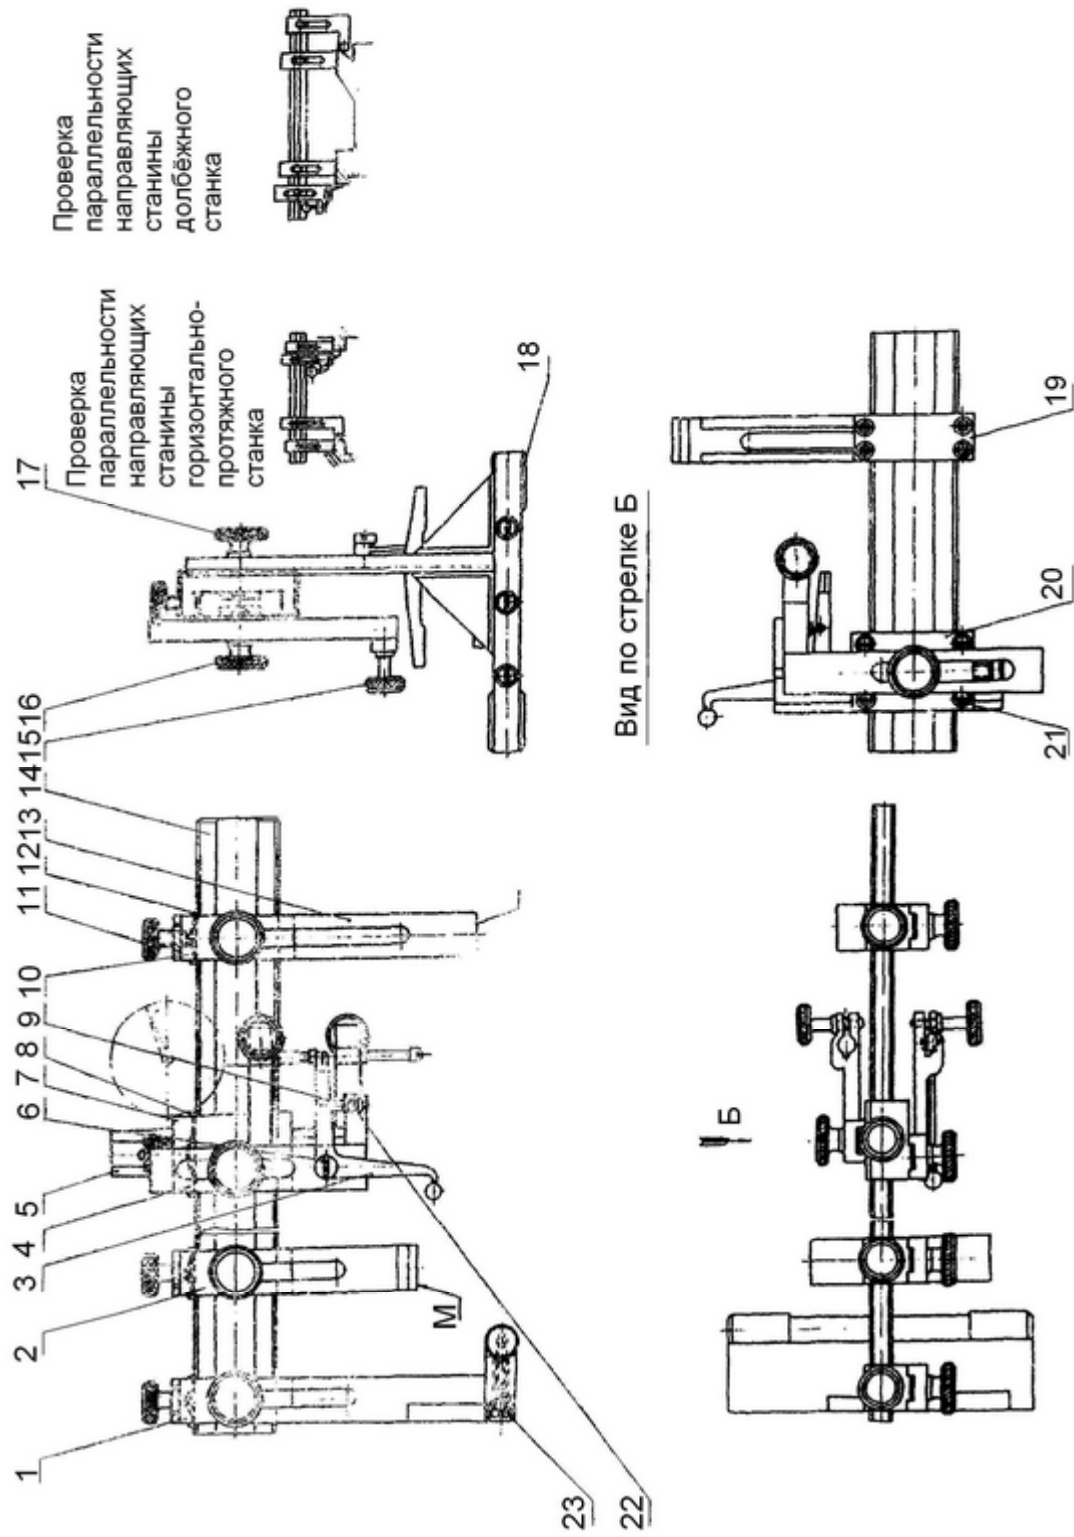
Приспособление для проверки параллельности направляющих СД 8532 – 4015
